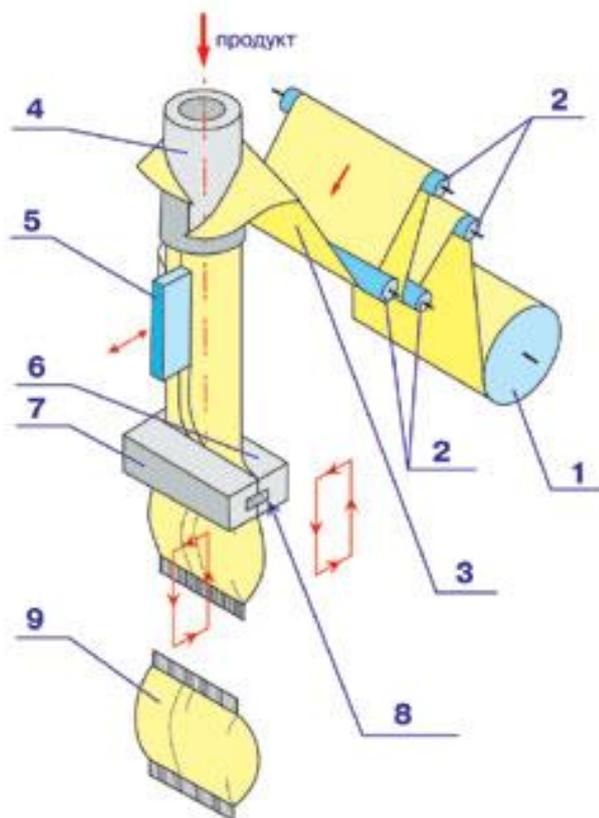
Схема воротниковой упаковочной машины периодического действия с тянущими губками поперечной сварки
